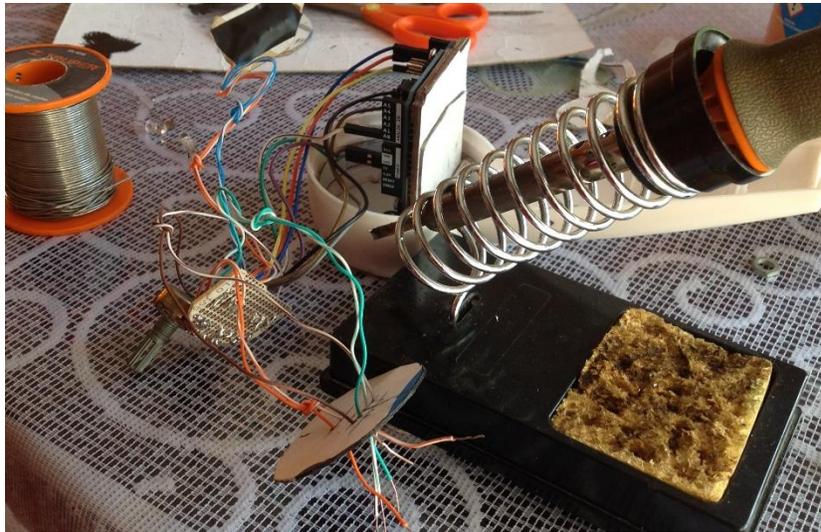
Proceso de soldar cables a la tabla fenólica.
